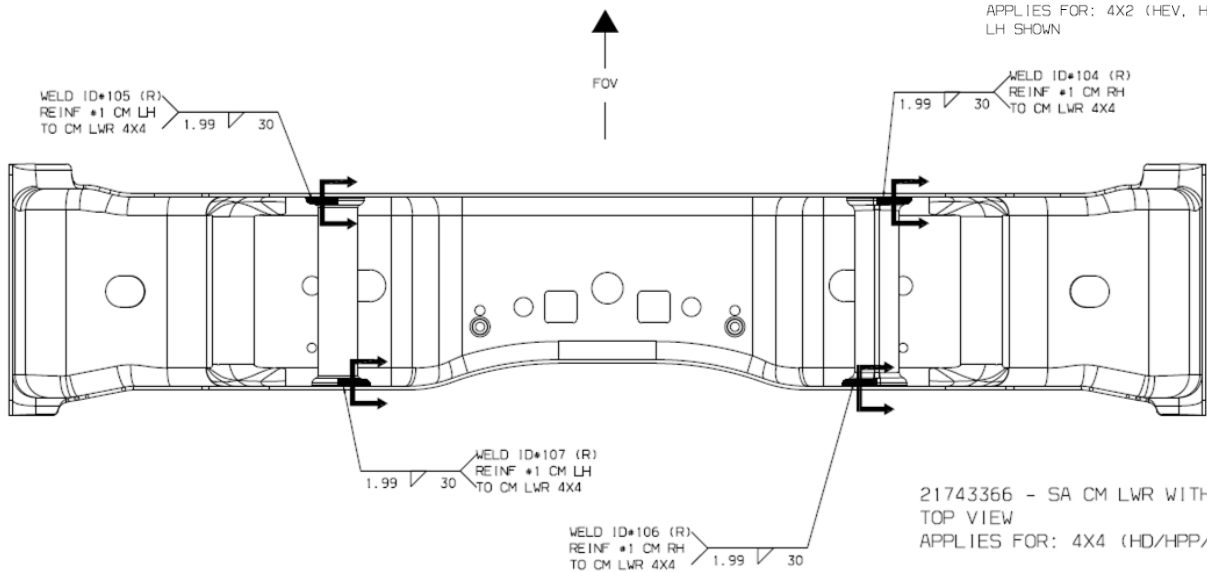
Sección 4, Información de Soldadura. [27]
